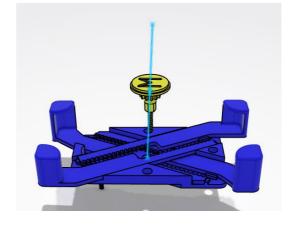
Ensamblar Rueda Dentada y Tornillo.
